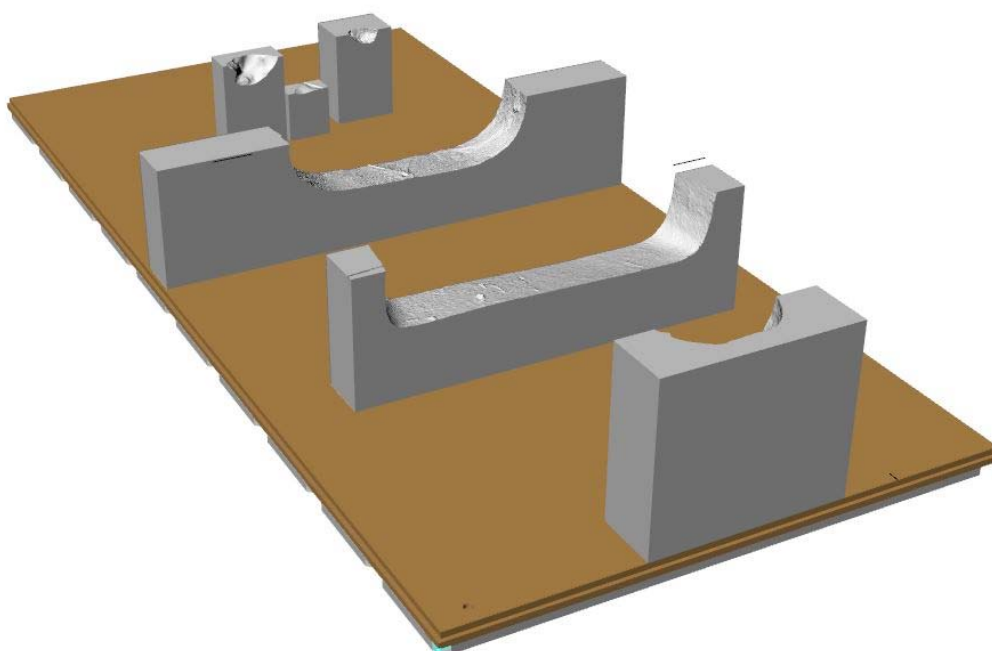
Posizionamento dei supporti sul piano di lavoro del Kuka (Rendering Rhinoceros)
